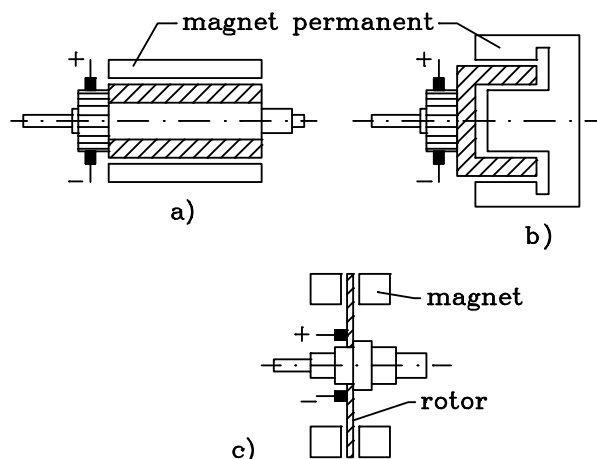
Schema principală: a) motor c.c. cu rotor cilindric; b) motor c.c. cu rotor "pahar"; c) motor c.c. cu rotor disc
